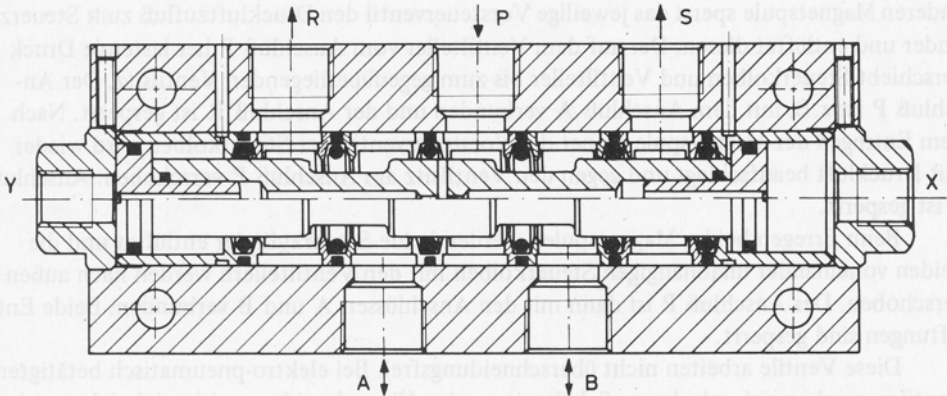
5/2-Wegeventil Kolbenschieber (Drumag)
